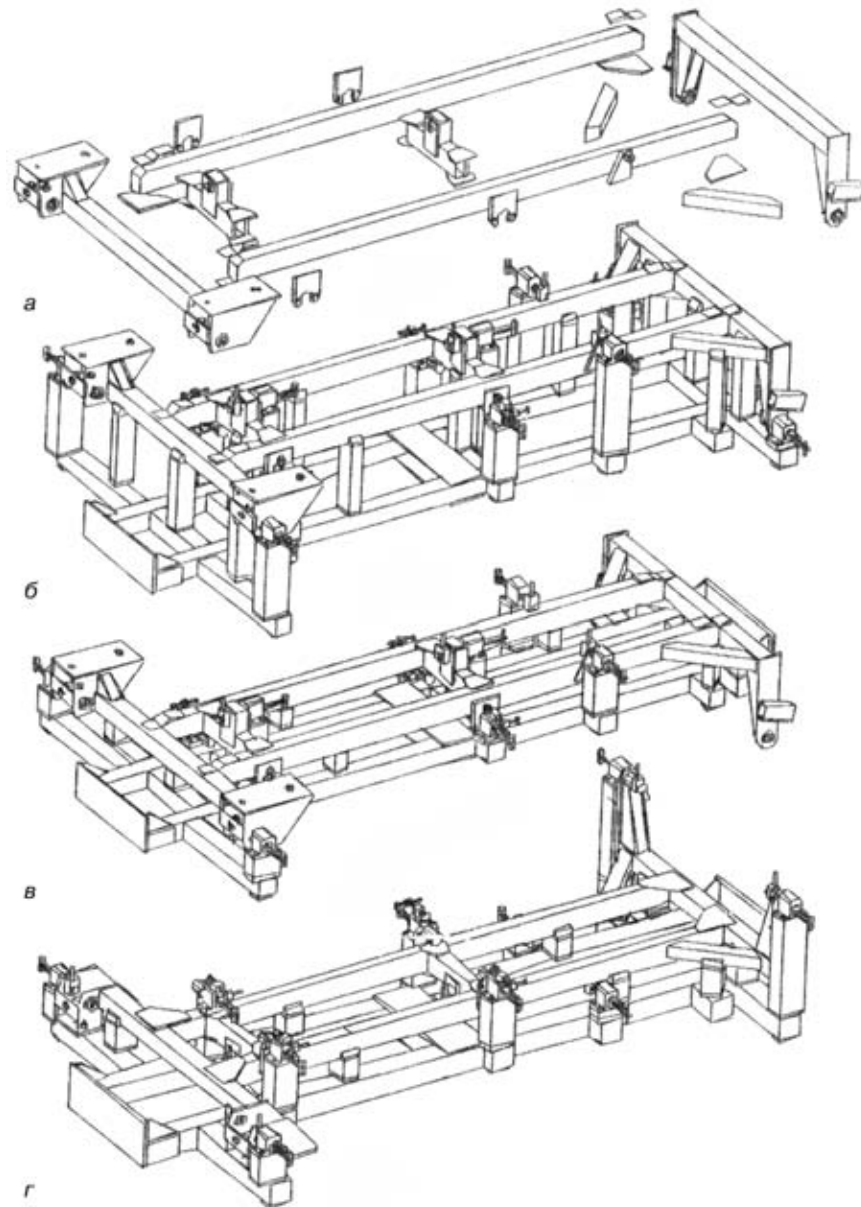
Схема сборки сварной конструкции (а) и варианты конструктивного воплощения сборочно-сварочного стенда с относительно высоким (б), предпочтительным положением центра масс ССЕ – ССП (в) и измененным положением ССЕ при сварке (г)
